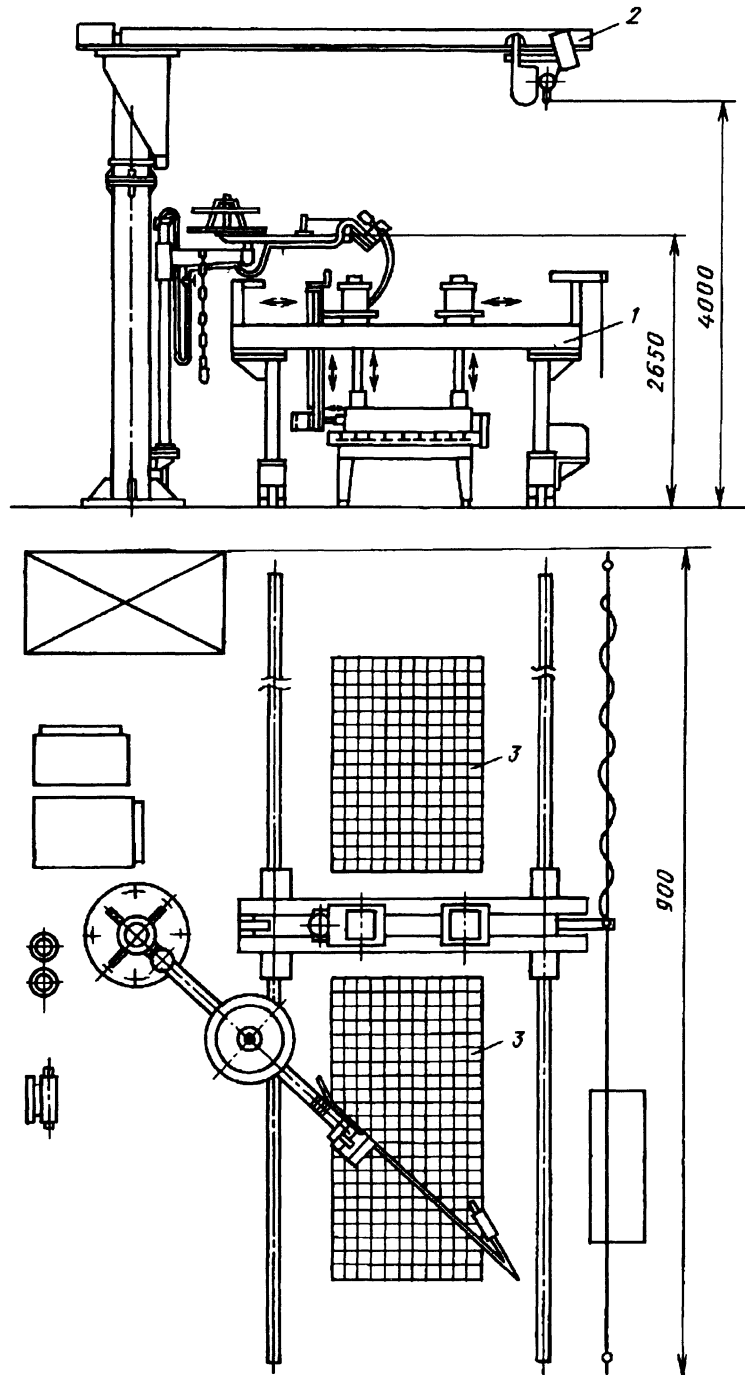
Типовое комплексно-механизированное рабочее место со сборочным порталом для сборки и балочных и коробчатых конструкций
